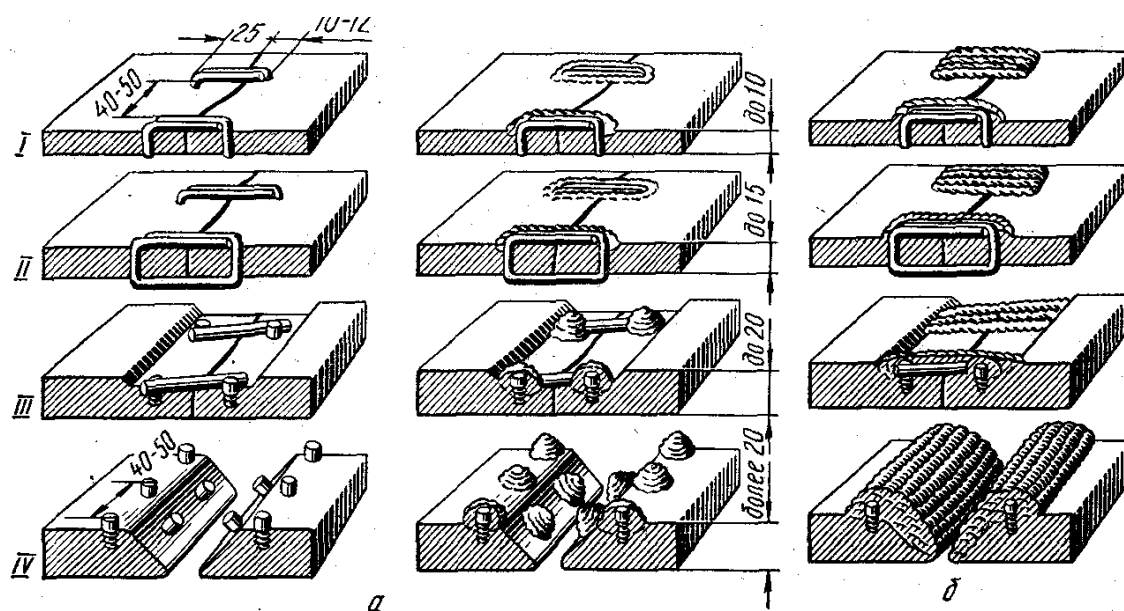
Зварювання чавунних деталей з постановкою штифтів і скоб: а — підготовка і початок обварювання; б — подальше й остаточне
